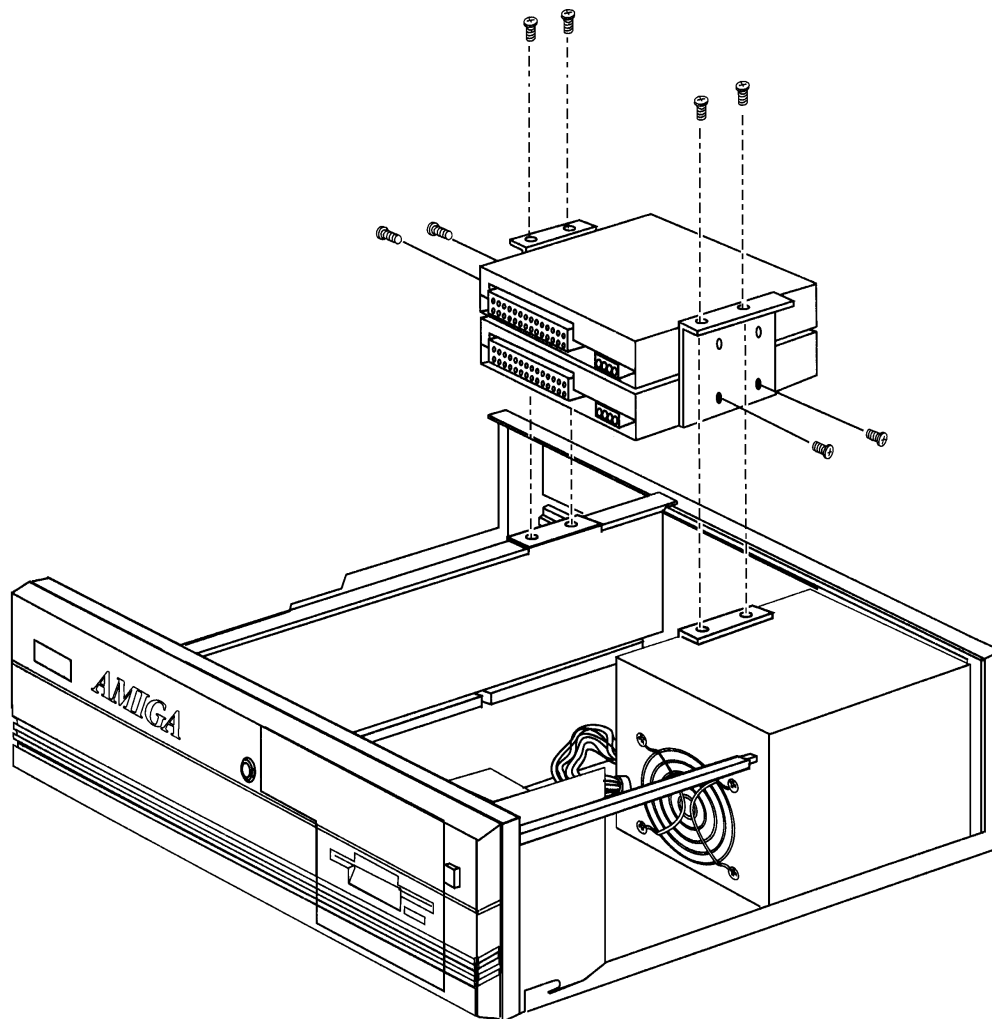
Entfernen der Halterung des hinteren Laufwerksschachts
